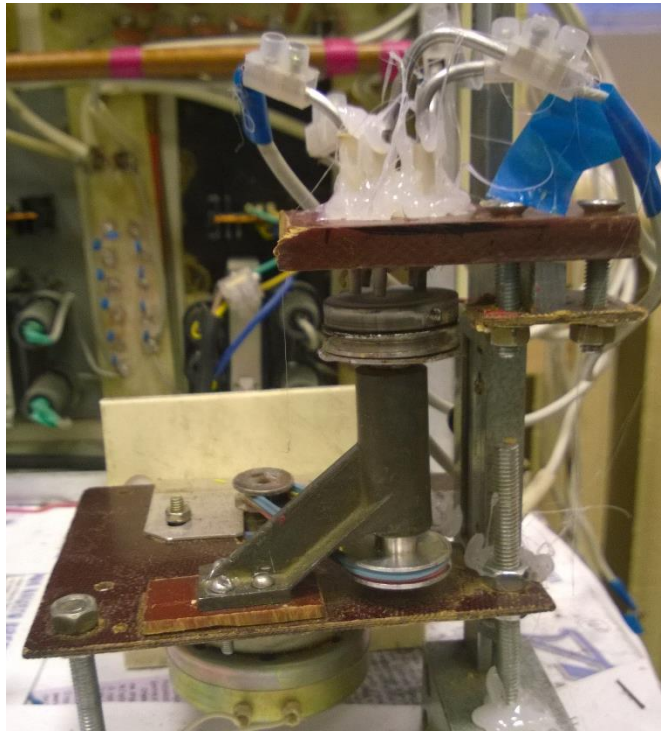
Приспособление для искрового упрочнения образцов
